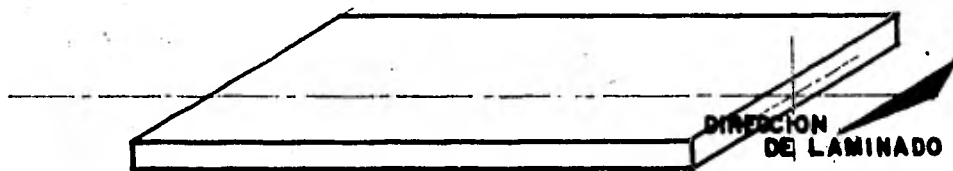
DIRECCION DE LAMINADO DE LAS PROBETAS DE PRUEBA
